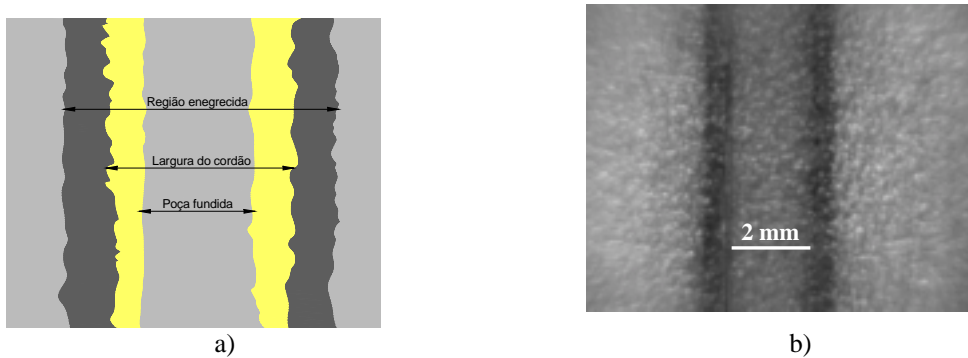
Largura do cordão de solda: a) esquema de medição b) vista superior
